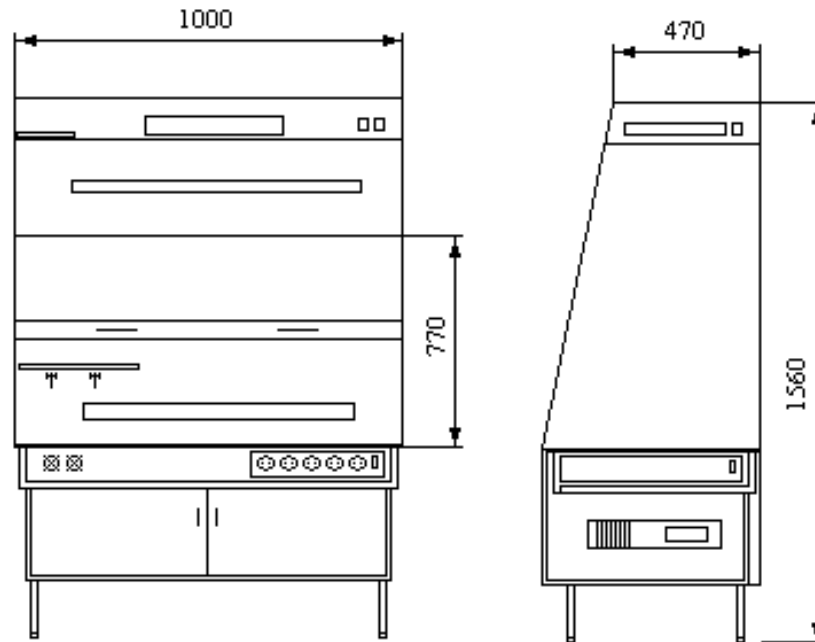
Витяжна шафа для виготовлення печатних плат
